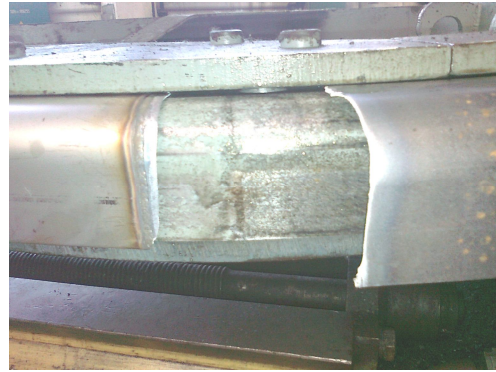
Разрыв сварного шва при гибке с растяжением дуг пассажирских вагонов из разнородных металлов
